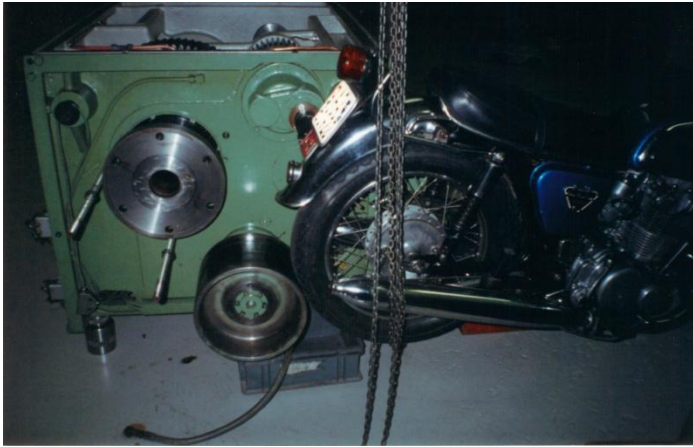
Noch einmal die Seitenansicht der Improvisation des Spindelstockes Testlauf der Heiligenstaedt Drehmaschine.
